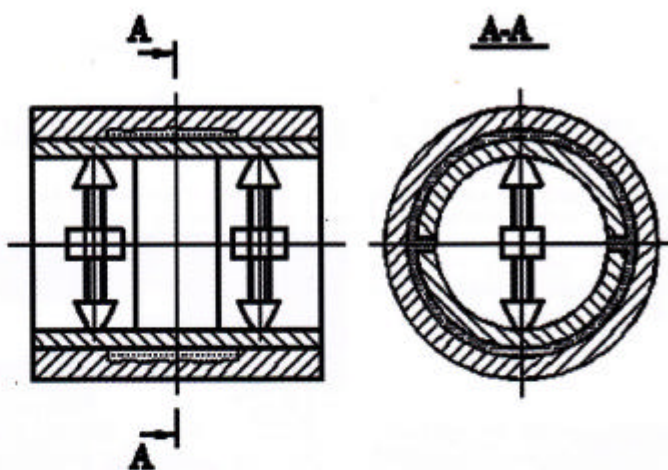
Восстановление поверхности посадочного места неразъемного гнезда подшипника с помощью стружки и разъемного шаблона
